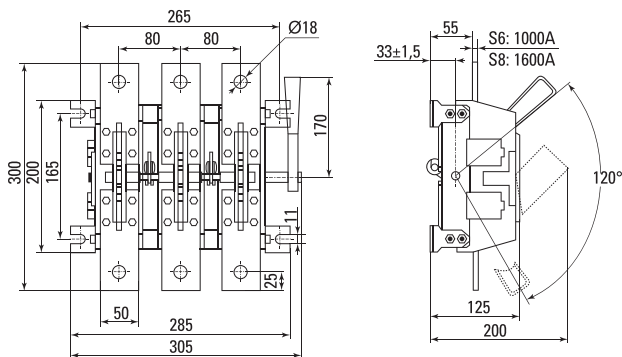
Габаритные и установочные размеры разъединителя типа PE19-41/43 с боковой рукояткой
